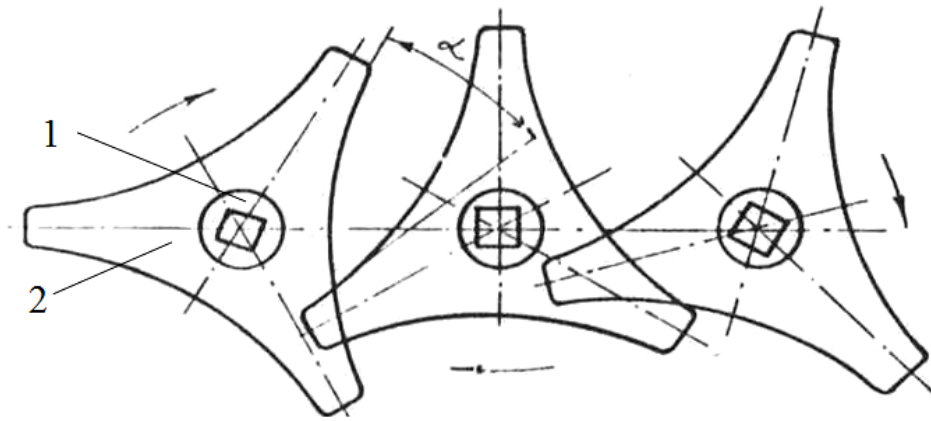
Конструктивна схема кулачкового очисника:
